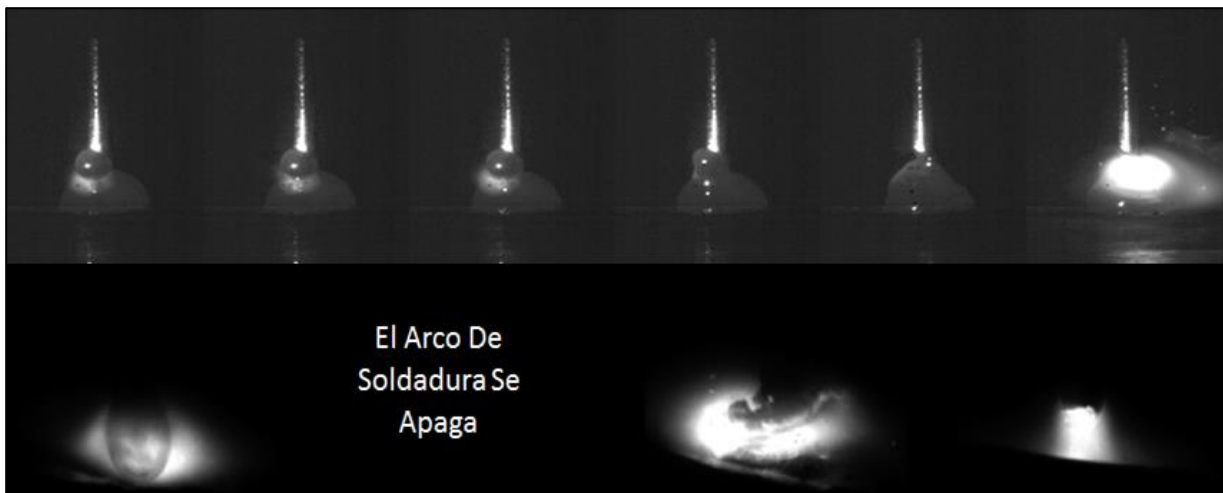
Ejemplo De Transferencia Por Corto Circuito En Soldadura [29 y 30].
